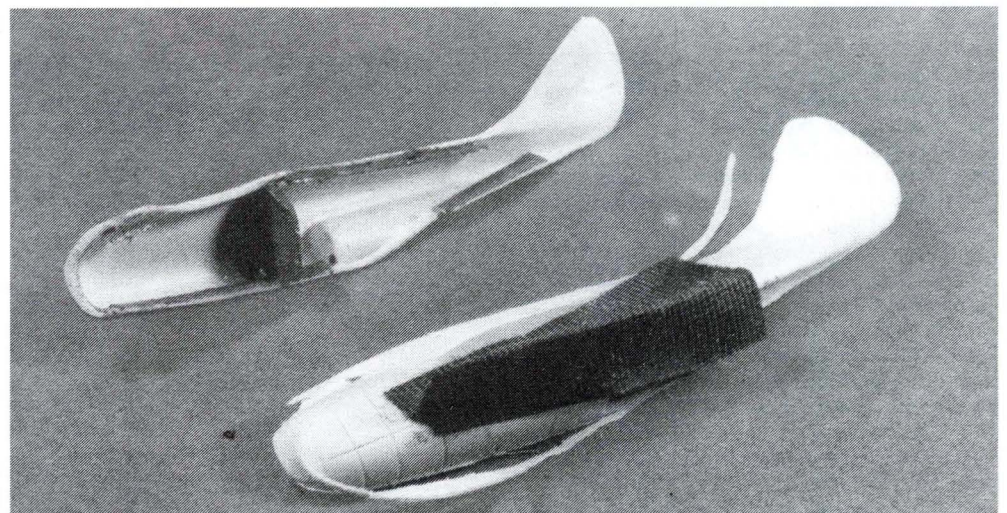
(rechts) Der Schleifspan löst sich ab, das Planschleifen ist beendet; (links) eingeleimte Verbindungslaschen und eingeleimter Querspan
